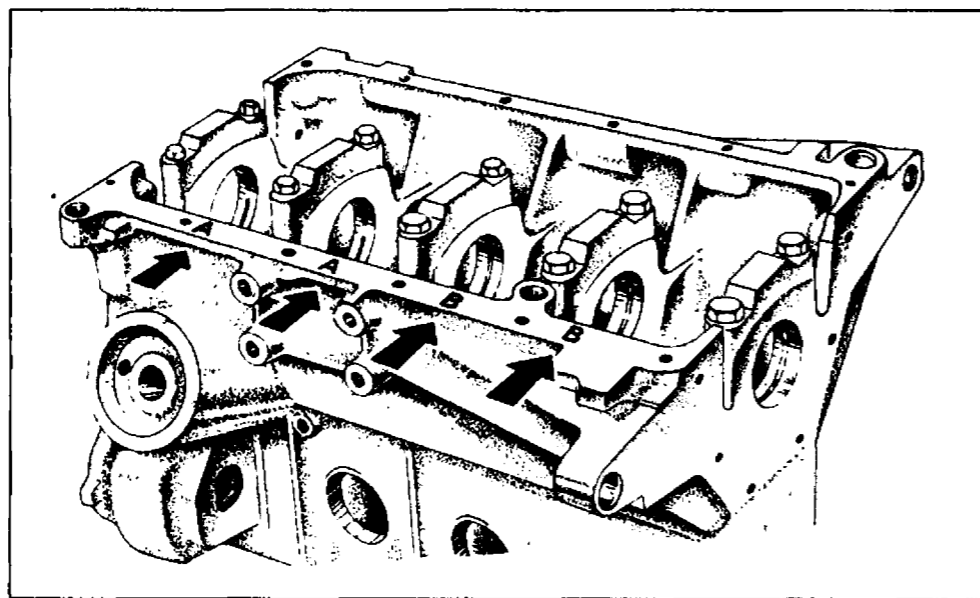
Маркировка размерного класса цилиндров на блоке
